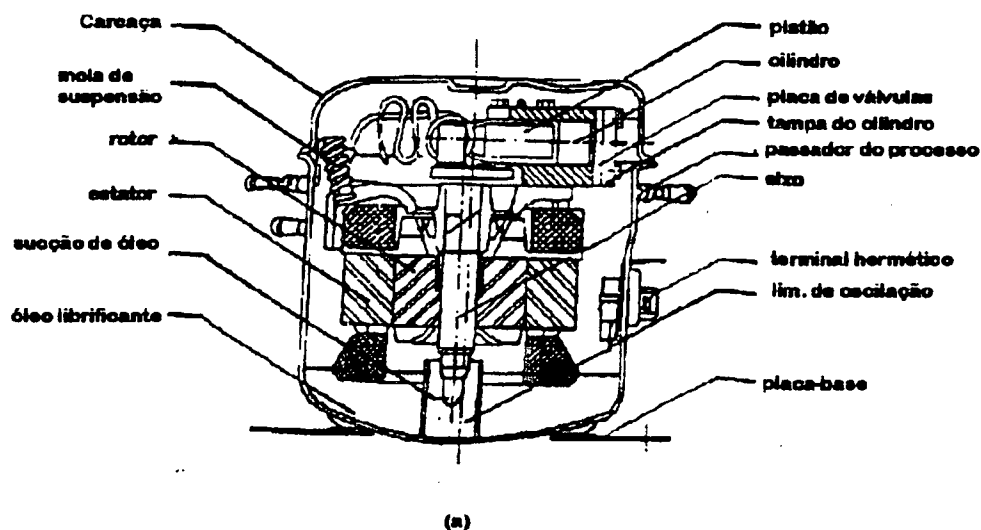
(a) Compressor PW 3.5K7 fabricado pela Embraco.
